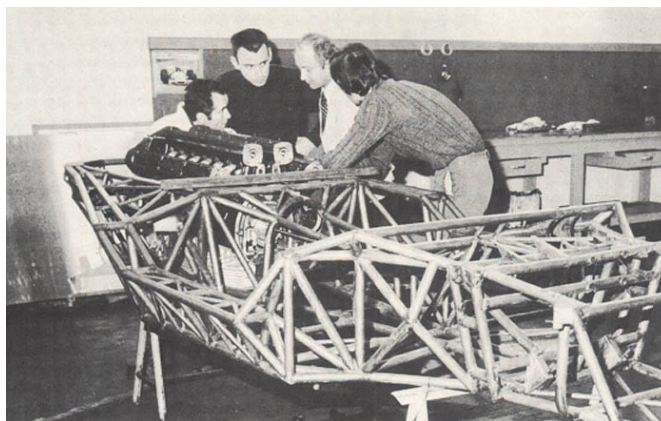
Chassi tubular utilizado no Lamborghini Countach LP 400 [22]
